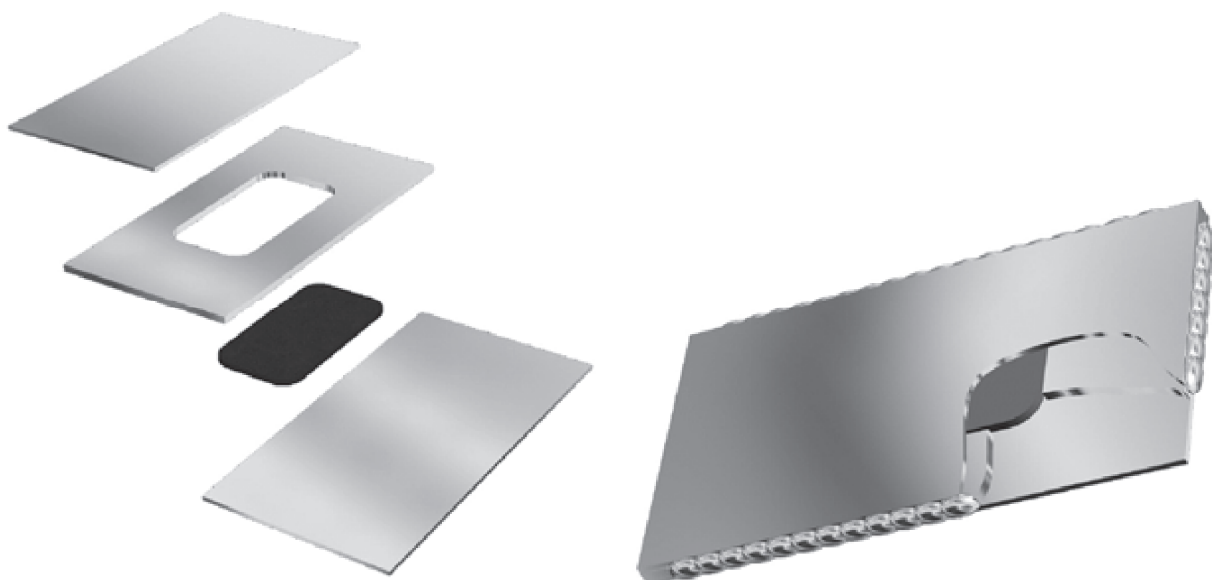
Technique du cadre photo: A) Assemblage B) Après soudage.
